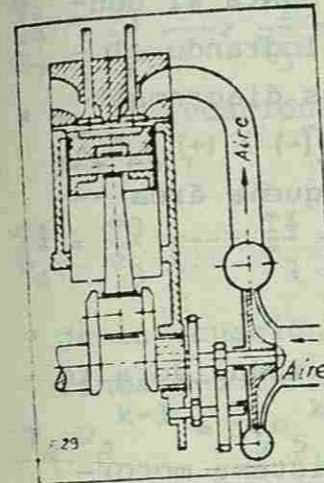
Compresor centrífugo accionado directamente por el cigüeñal del motor.
